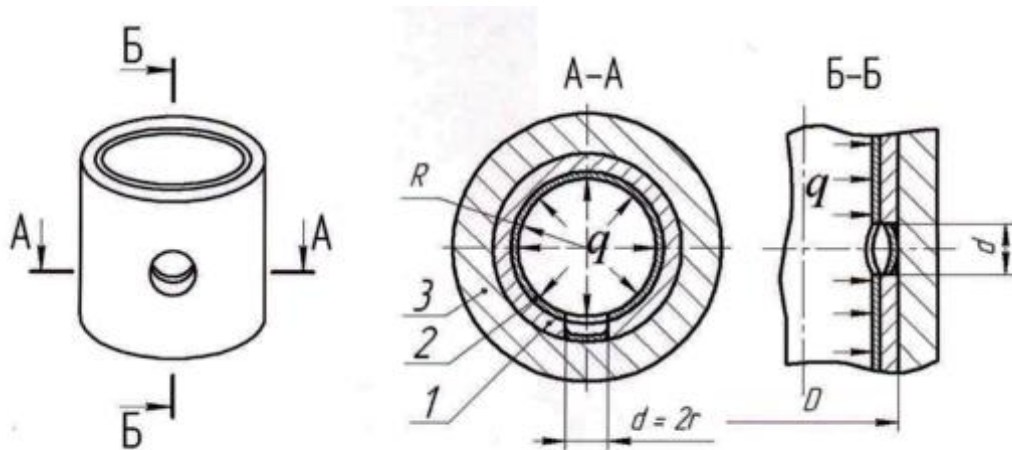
Схема процесса пробивки отверстия в трубчатой заготовке, где 1 – матрица; 2 – труба (заготовка); 3 – технологическая обойма; q – давление эластичного инструмента
